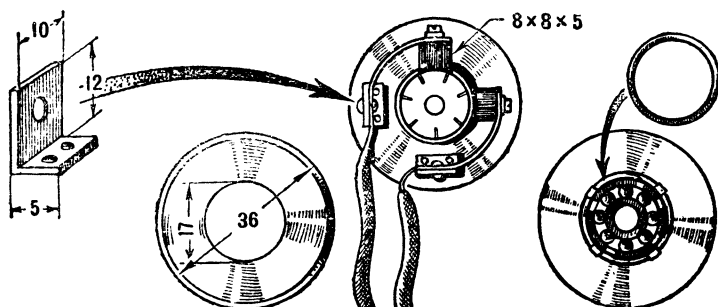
Детали и конструкция щеткодержателя. Крепление щеткодержателя на обойме с помощью кольца.
